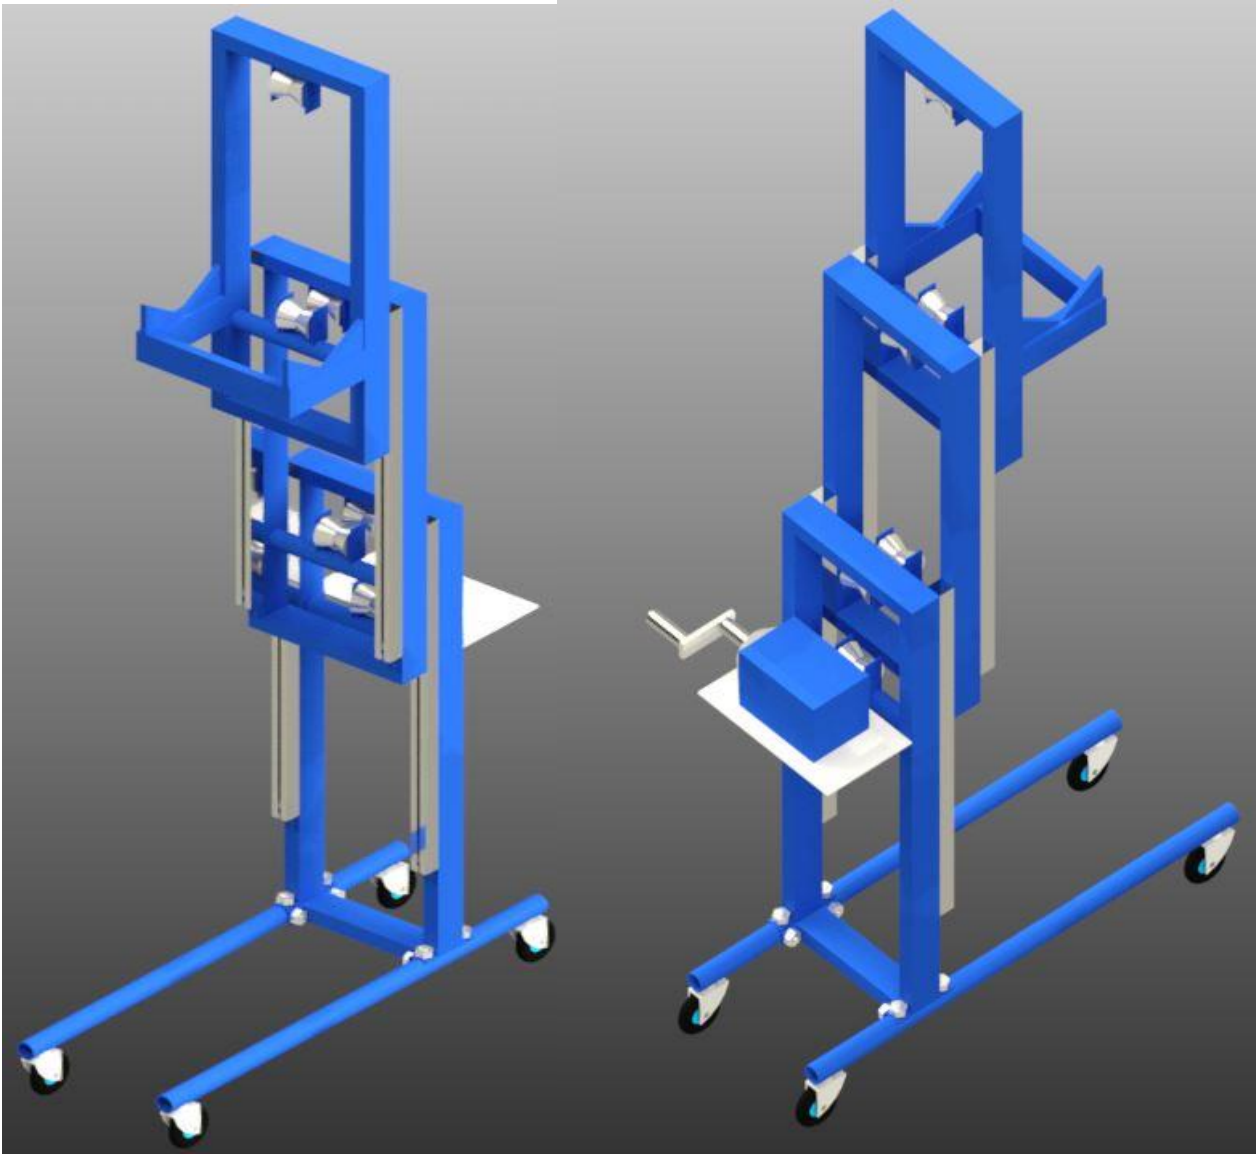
Vista frontal y posterior del elevador de tubería. Elaboración propia (2020)
